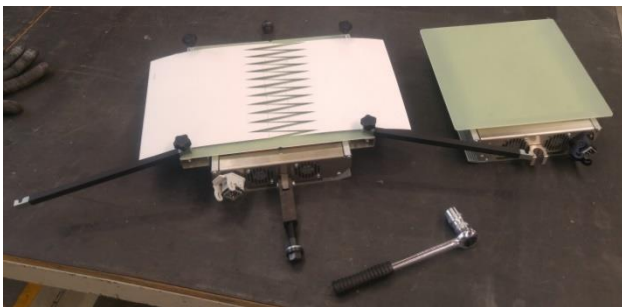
Posizionamento nastro Fabric su piastra di giunzione
